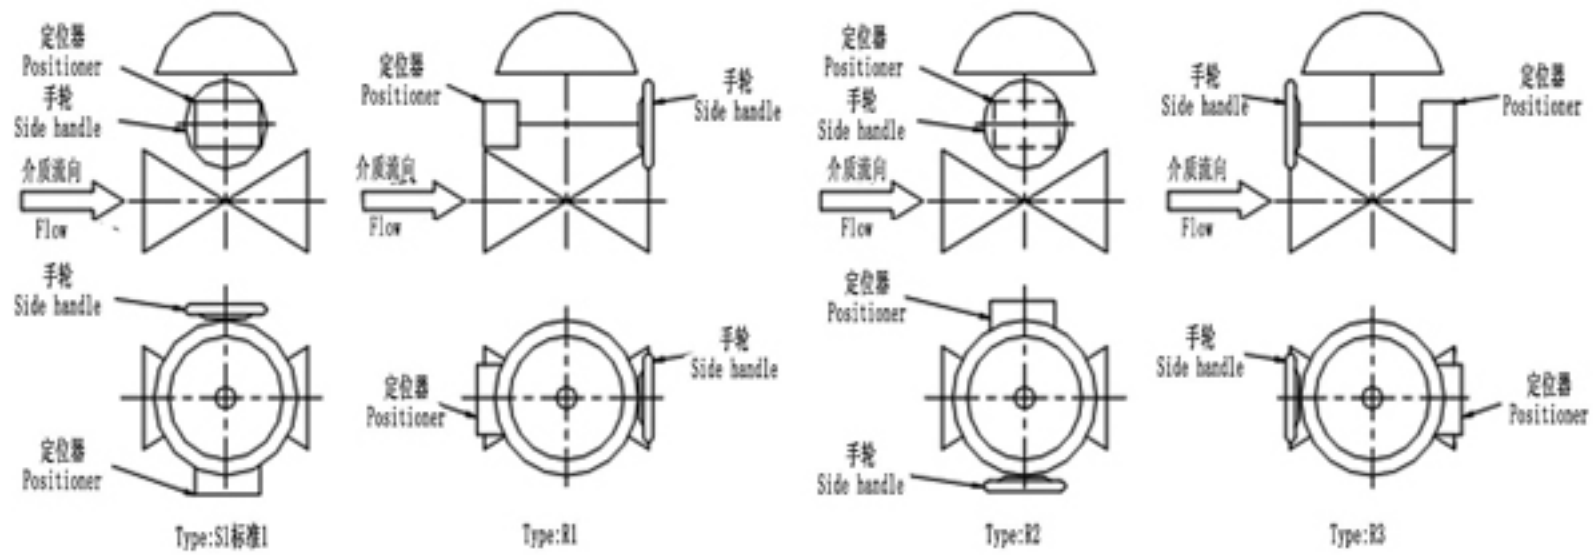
配 MF5 执行机构的安装位置 Fig.5-2. Mounting forms with MF5 actuator
